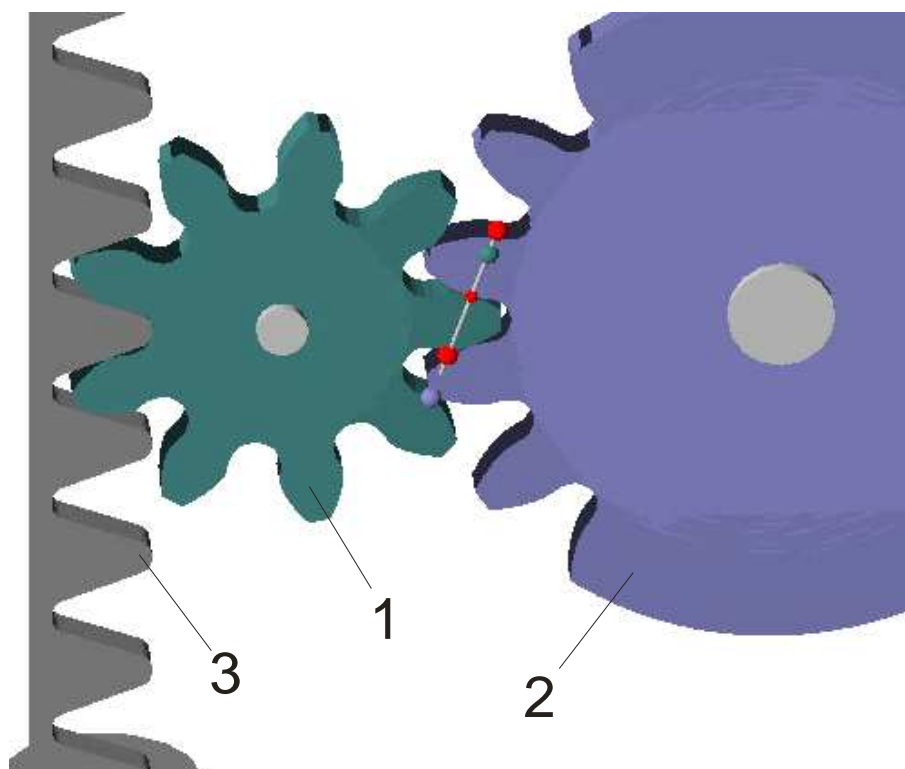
Зацепление зубчатого колеса 1 с колесом 2 и зубчатой рейкой 3
